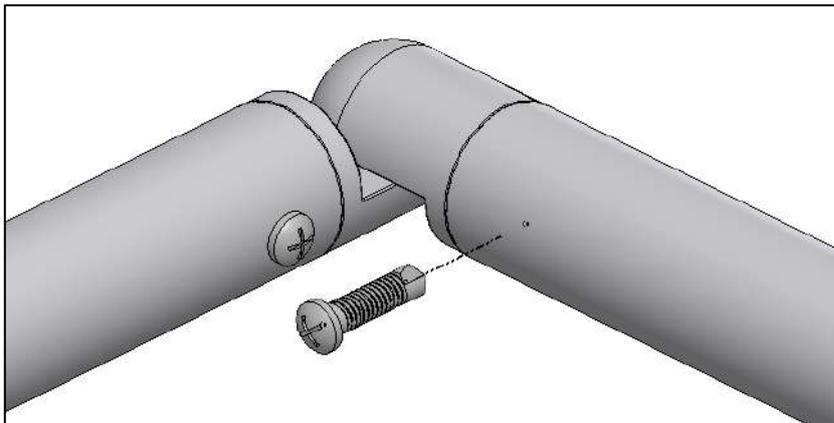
Instalación del manguito articulado entre los propios barandales en las esquinas de la cubierta mediante tornillos autorroscantes.
